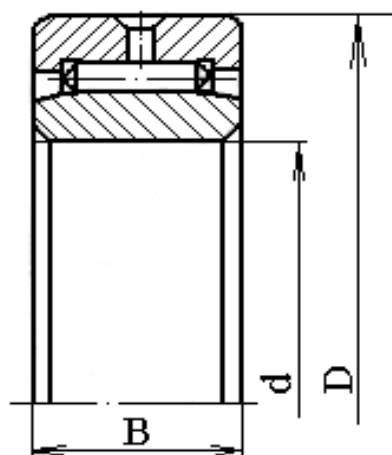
Подшипник роликовый с длинными цилиндрическими роликами
